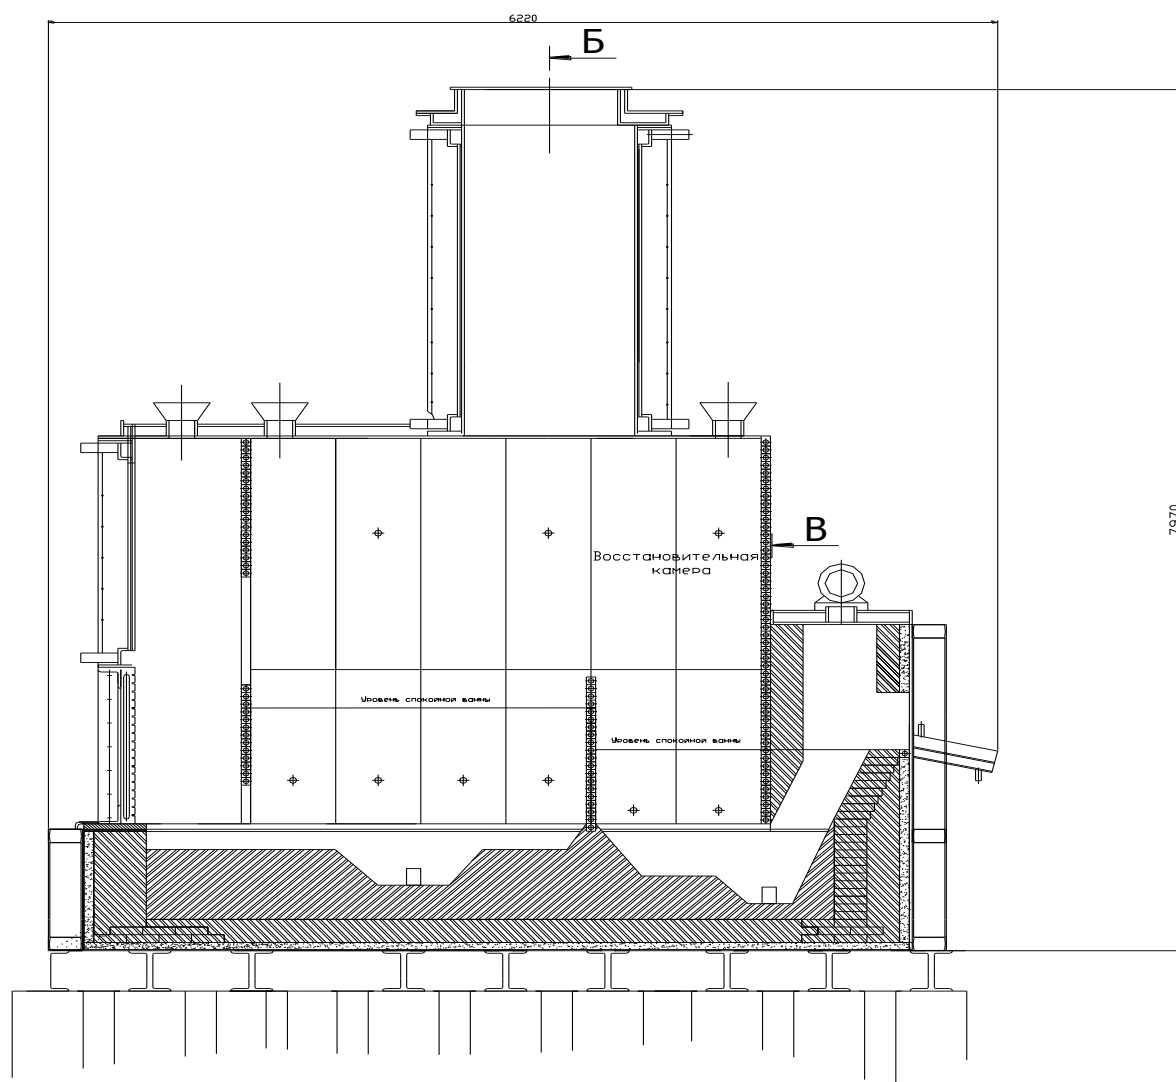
Двухкамерная печь Ванюкова с загрузочной камерой и приемком для выпуска чернового металла
